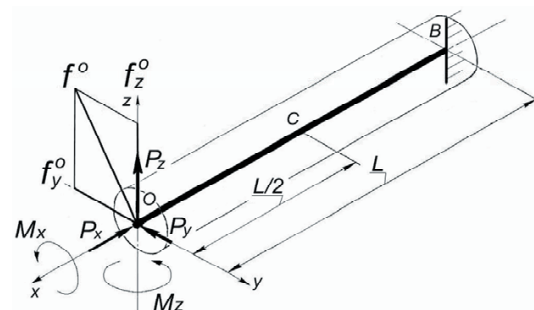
Розрахункова схема заготовки, яка обробляється на токарному верстаті
